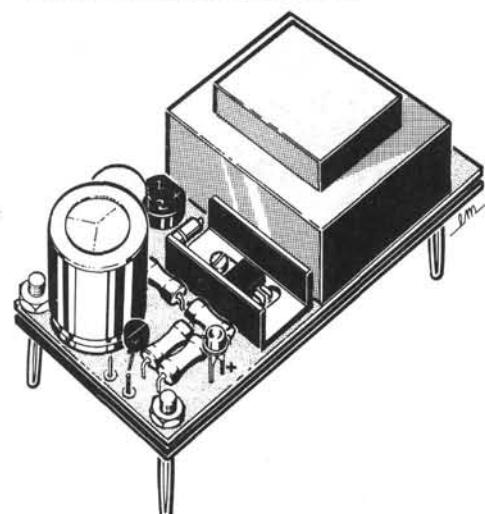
Le montage des deux plaques en sandwich est visible sur cette perspective cavalière. Le cordon secteur, soude sur les plages de cuivre, est pincé entre les deux plaques d'époxy. Il ne sera dénudé que sur la longueur strictement nécessaire à la soudure.
